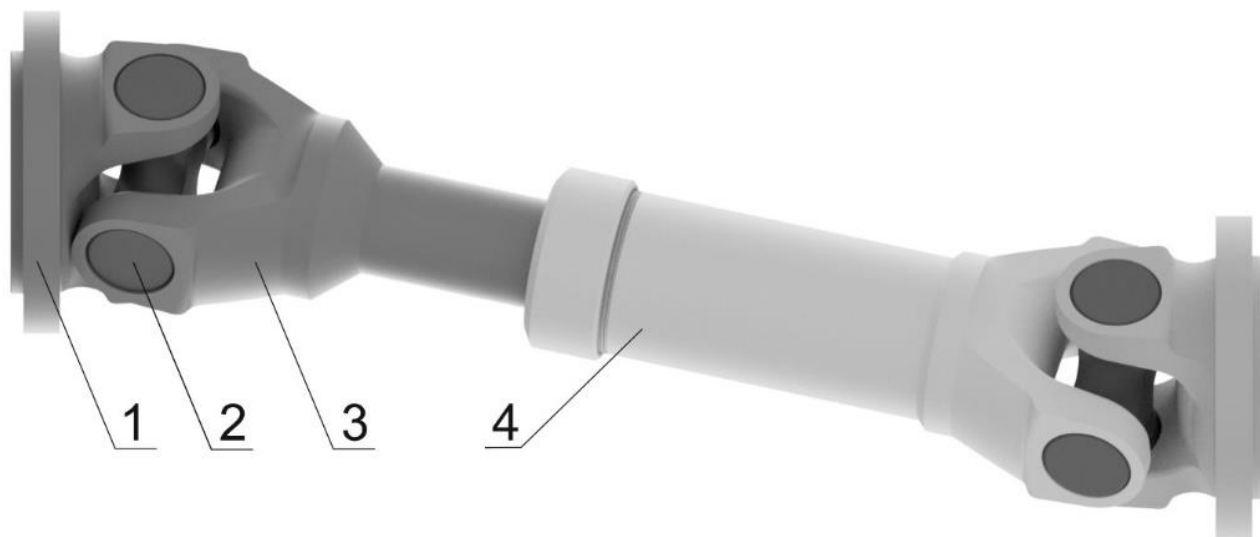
Схема карданной передачи: 1 – фланец; 2 – крестовина шарнира; 3 – вилка; 4 – скользящая вилка
